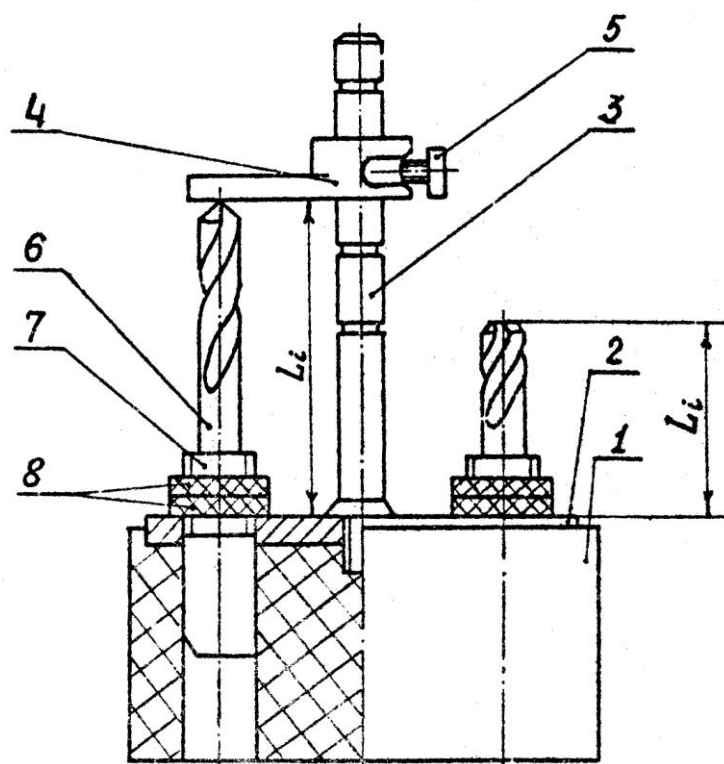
Прибор флажкового типа: 1 – корпус; 2 – плита;
